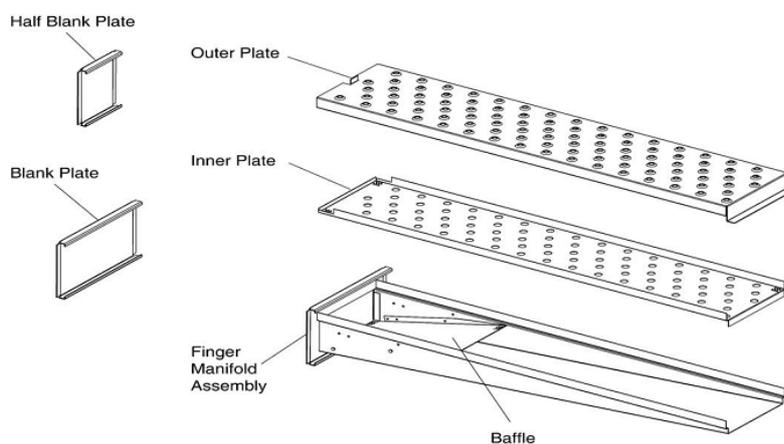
Необработанные крышки (двух размеров) и направляющие воздуха
